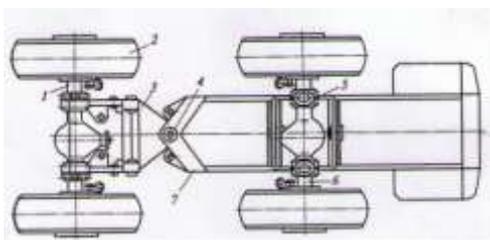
Компоновка двухосного шасси с шарнирно-сочлененными поворотными полурамами
